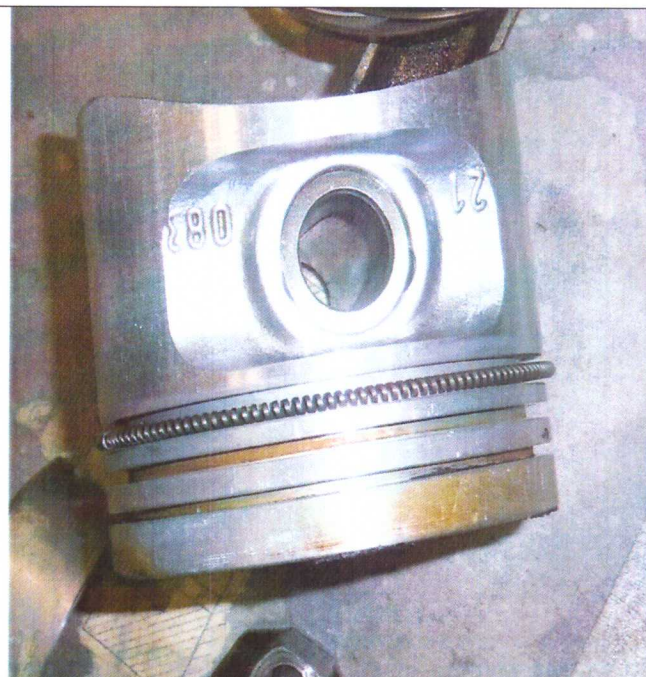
Внешний вид боковой поверхности поршня первого цилиндра по окончании длительных испытаний двигателя при работе на базовом масле Castrol EDGE
